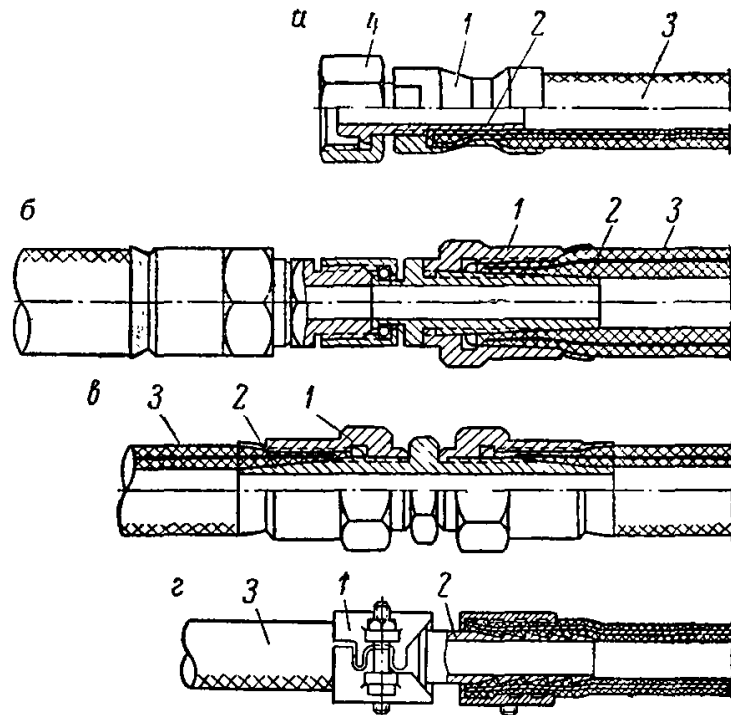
Устройства для соединения гибких высоконапорных резиновых рукавов с металлическими оплетками:
